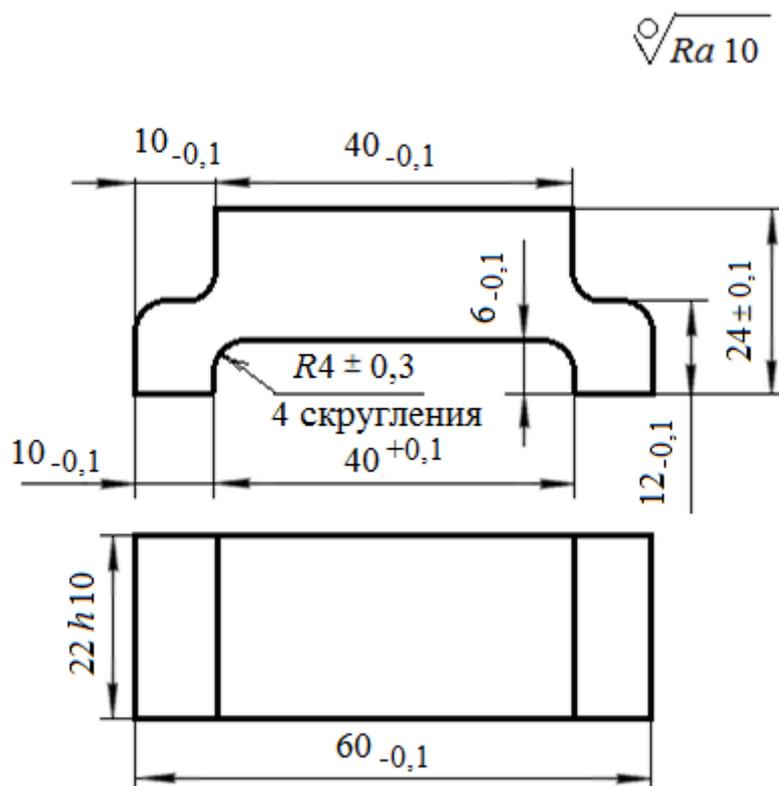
Эскиз исходной заготовки для детали «Планка»
